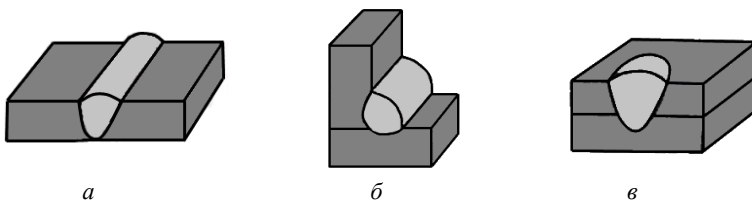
Классификация сварных швов по форме поперечного сечения:
